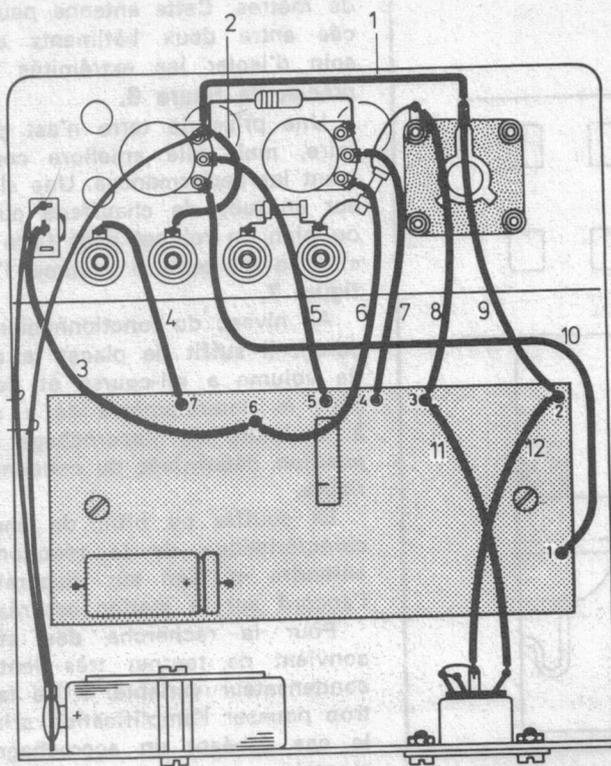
et 5. — Sur ce plan de câblage général on distingue parfaitement l'emplacement du circuit imprimé monté sur deux entretoises de 10 mm sur le fond du châssis. La prise DIN placée sur la face arrière servira avec son support adéquat à la réception des bobines interchangeables.
